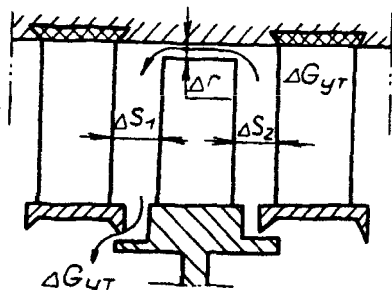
Схема зазоров в ступени осевого компрессора
